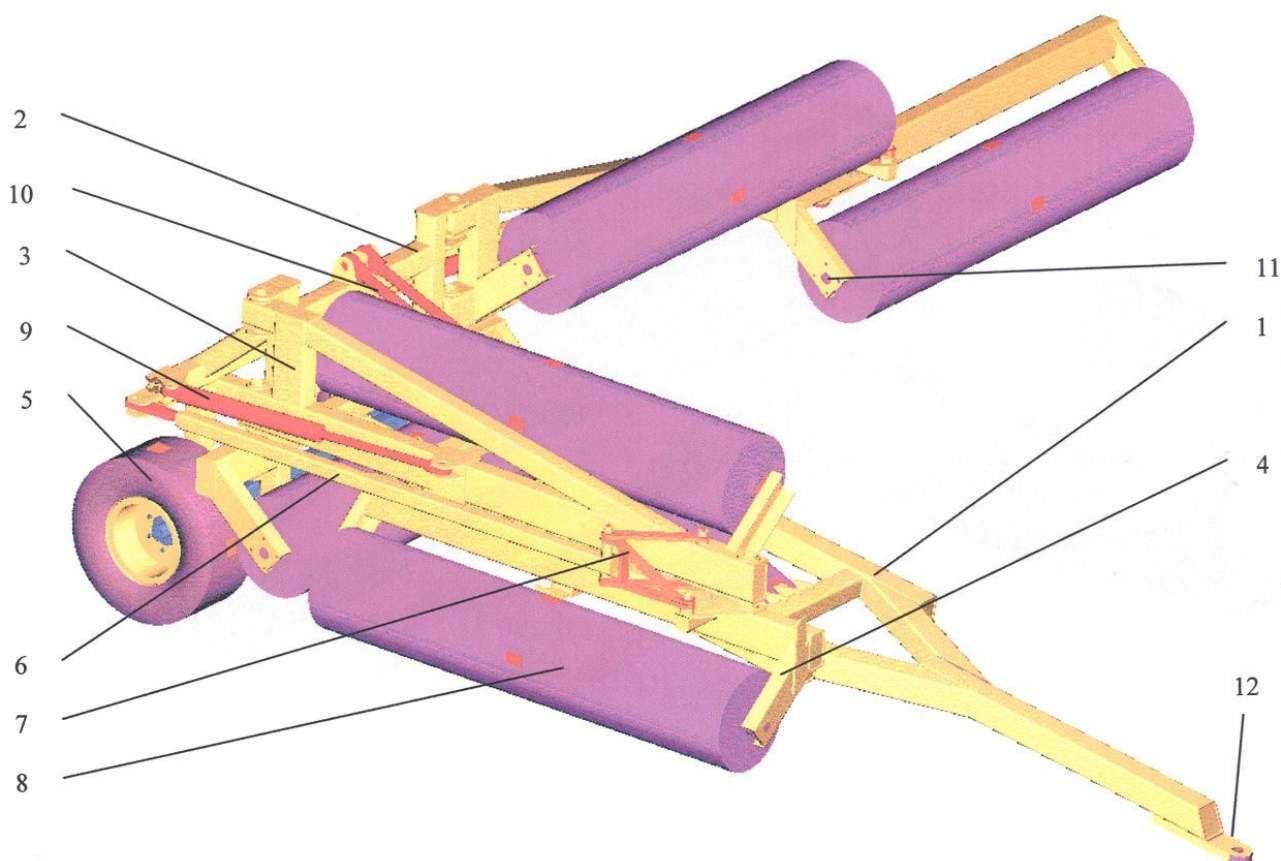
Общий вид полевого обрабатывающего катка MAXIMUS.
